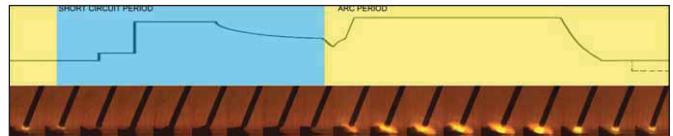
График сварочного тока в процессе сварки FastROOT™. Капля металла с кончика проволоки переносится в сварочную ванну. Чередуются периоды короткого замыкания и горения дуги
